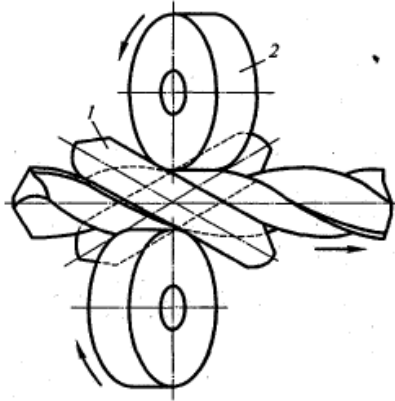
Схема повздовжньо-гвинтової прокатки свердла:
